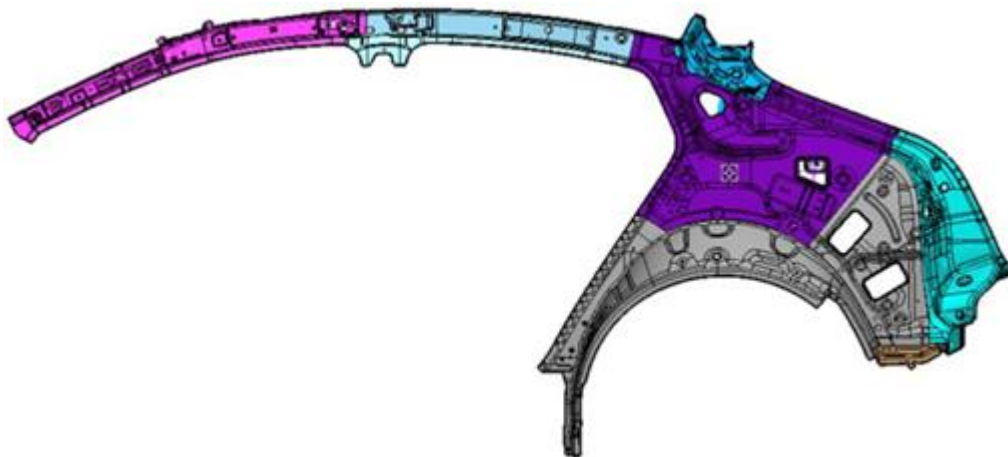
Bodový plán robotického odporového svařování ve stanici 3280 (R02) [13]
